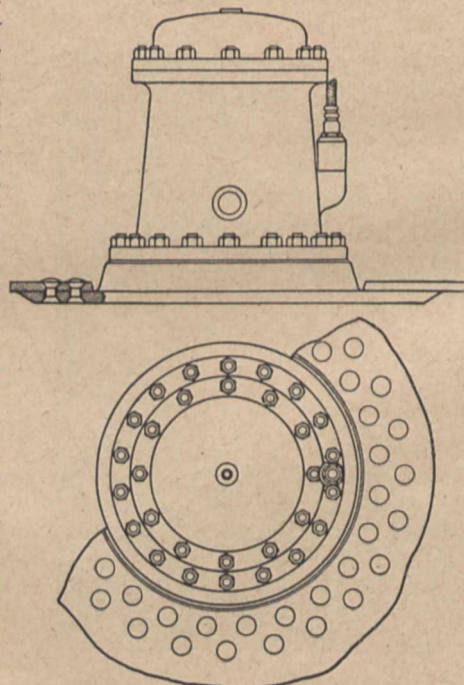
Flansch-Sender zum Einbau in die Bordwand.
